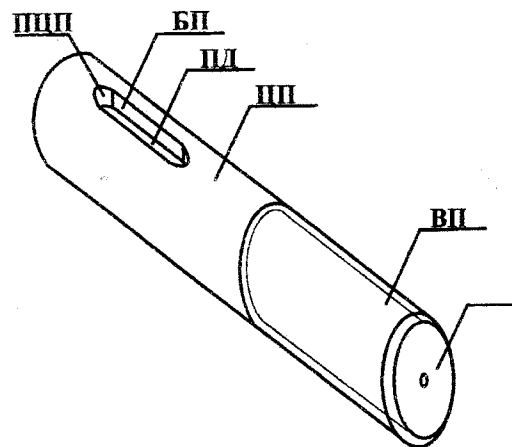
Тестовая деталь для ТВС и ВФС: ПЦП – боковая полуцилиндрическая поверхность; БП – плоская боковая поверхность; ПД – поверхность дна; ЦП – цилиндрическая поверхность; ВП – винтовая поверхность; ППТ – поверхность плоского торца
